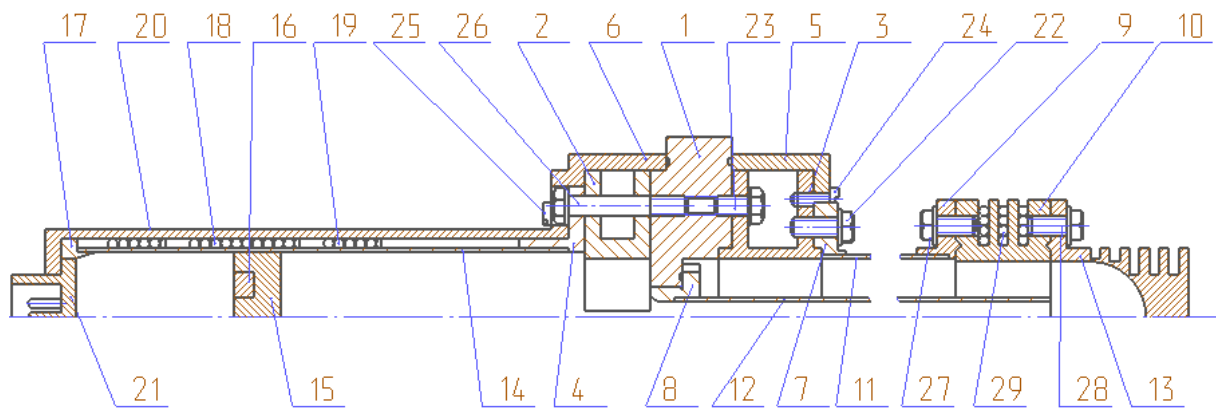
Чертёж общего вида проектируемого макета двигателя
